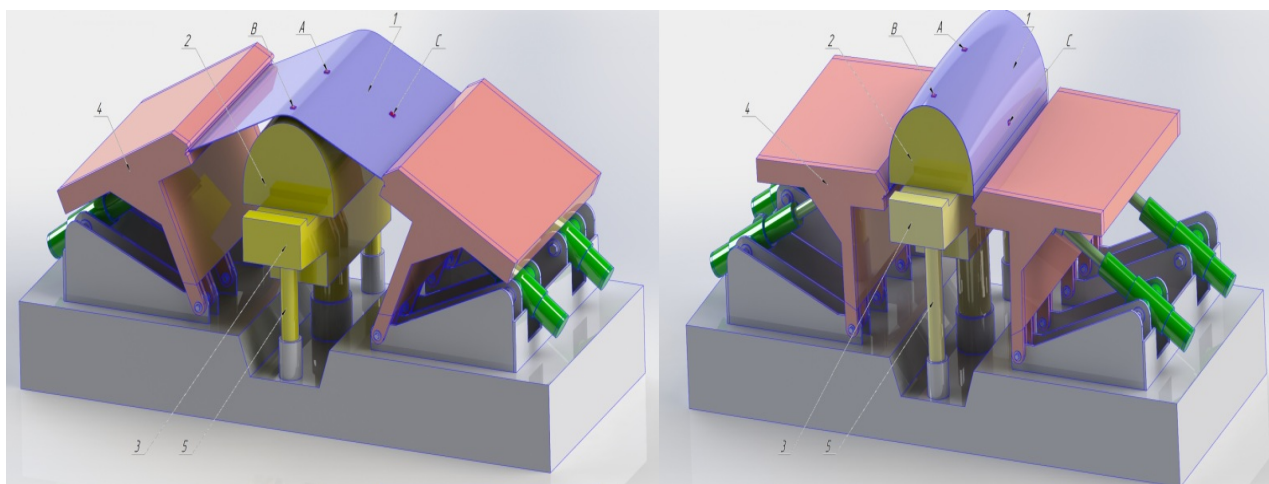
Схема предварительной обтяжки после обвертки плоской листовой заготовки обтяжного пуансона по формообразующему контуру на полный угол охвата α_k , равный 90°
